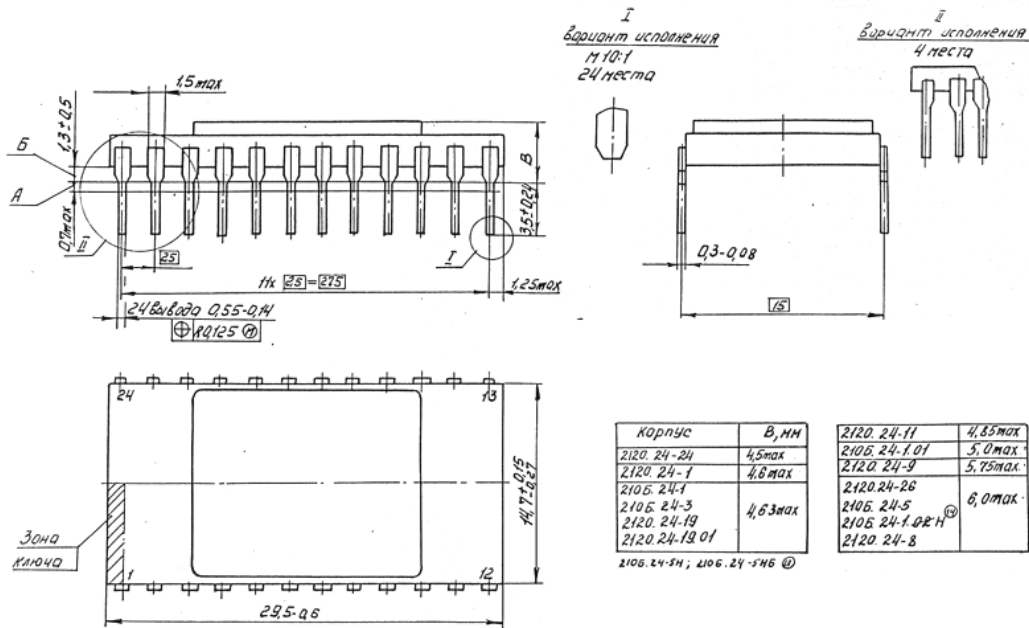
Габаритный чертеж корпуса 210Б.24-1
